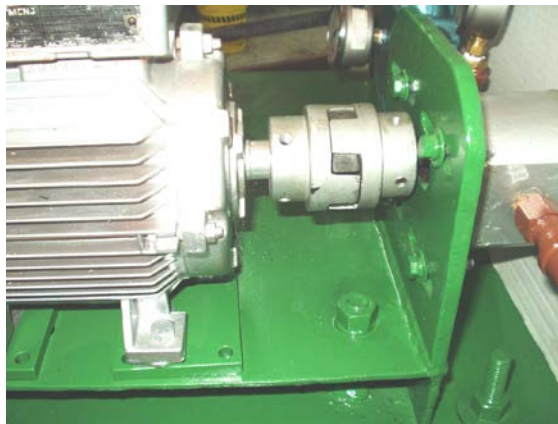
Acople del motor y la bomba. Fuente: Propia.
